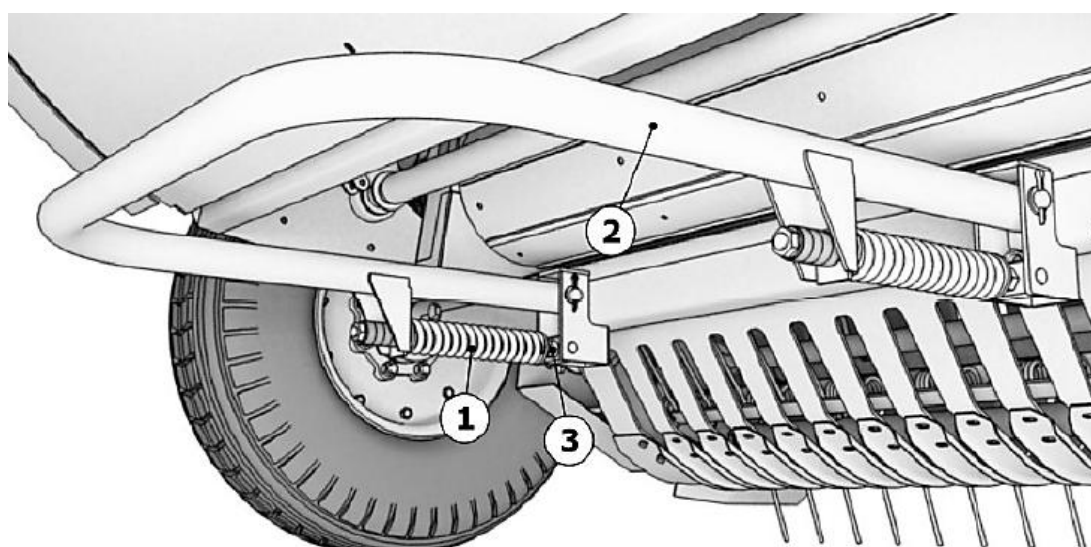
Регулировка скатной горки: 1 – пружина; 2 – скатная горка; 3 – гайка регулировочная
